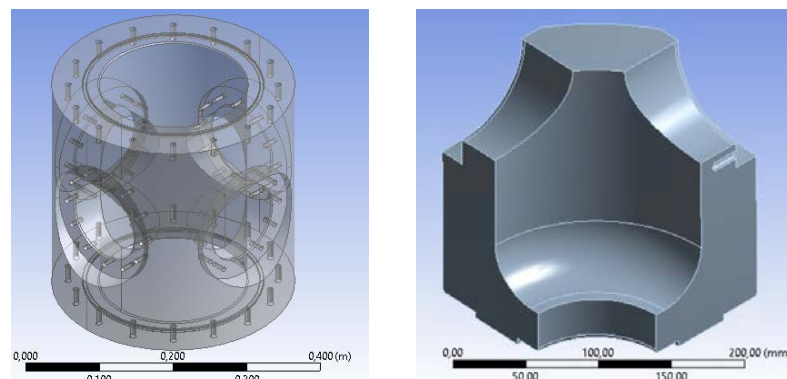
CAD del cilindro (izquierda) y sección utilizada (derecha)
